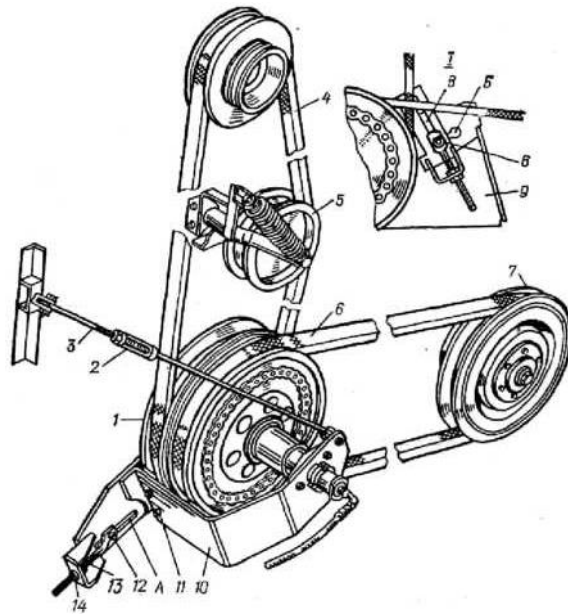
Ходовий варіатор: 1 - ведучий блок; 2 - гайка; 3 - розтяжка; 4 - приводний пас; 5 - натяжний ролик; 6 - нас; 7 - ведений диск; 8, 12 - шпильки; 9 – плита; 10 - каркасна рамка; 11 - болт; 13, 14 - гайки; I - плита кріплення каркасної рамки (коefficient варіації - 2,85; діаметри шківів: приводного ведучого блока - 460 мм, варіатора ведучого блока 280-456, веденого блока 242-419 мм; частота обертання ведучого блока - 1208, веденого - 798-2272 об/хв.).
